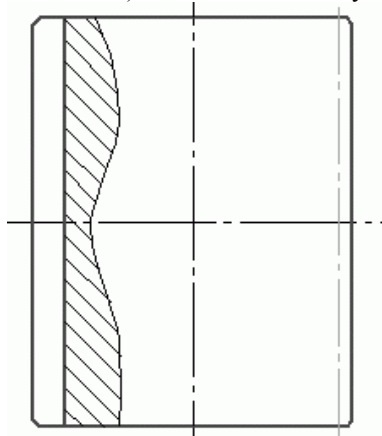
Полученная зубчатая шестерня (слой с изображением зубчатого колеса погашен)
